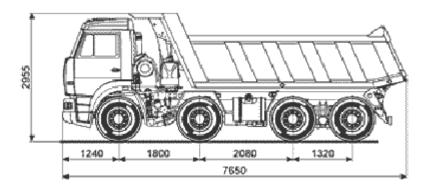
Габаритные размеры самосвала КамАЗ – 6540
